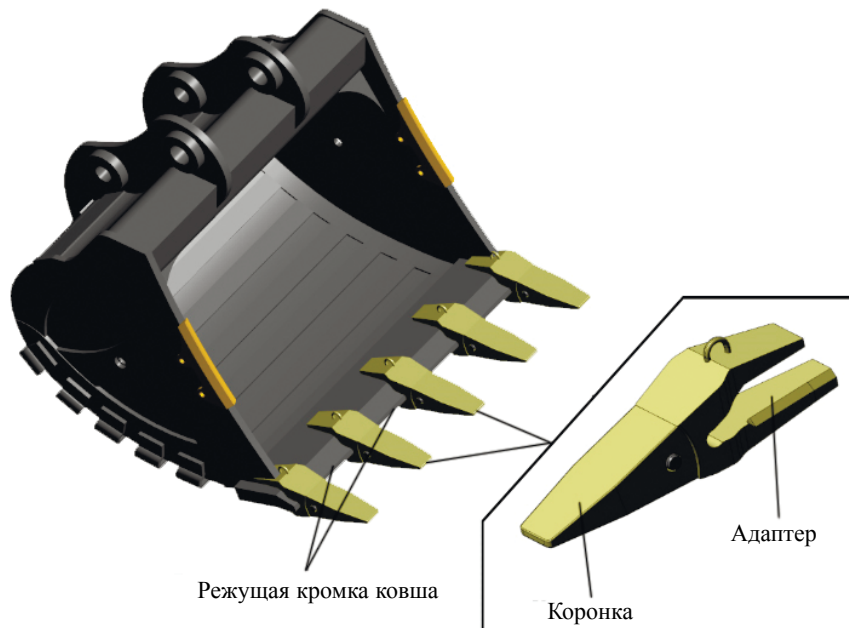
CAD-сборка ковша Komatsu PC400LC-7.
